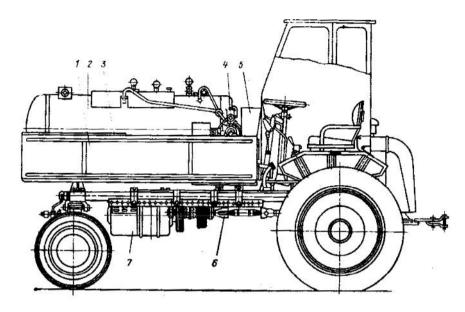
Самоходная установка для ремонта покрытий: 1 – платформа самоходного шасси; 2 – ресивер; 3 – ящик для ручных машин и инструмента; 4 – компрессор; 5 – пульт управления; 6 – трансмиссия; 7 – генератор
